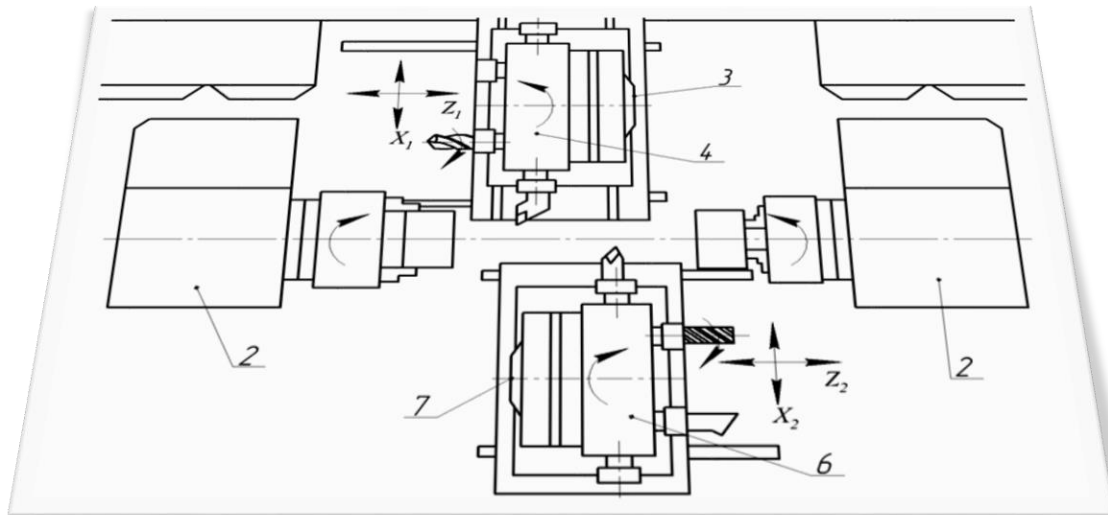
Схема оброблення на 2-шпиндельному токарному верстаті з ЧПК
